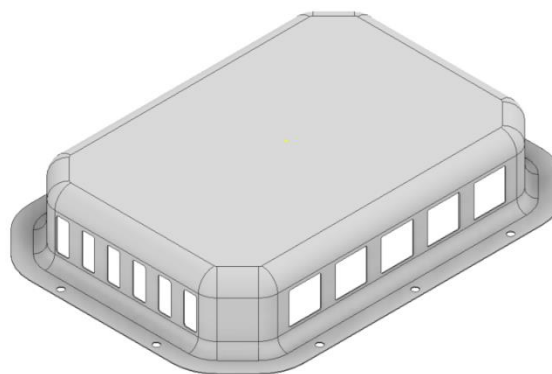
Příklady výtažků [5; 6; 7; 8].
